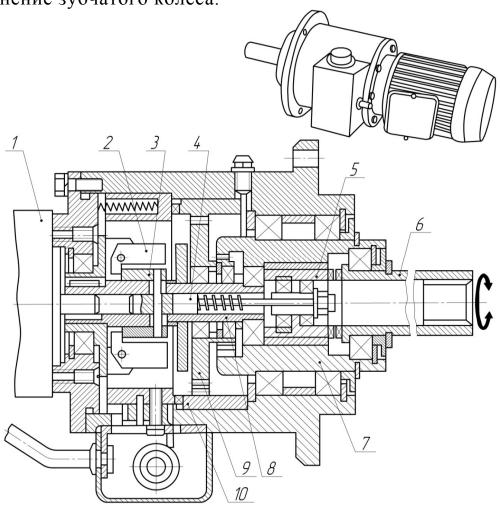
Электромеханический привод: 1 – электродвигатель; 2 – рычаг; 3 – втулка; 4 – шток; 5 – муфта; 6 – шлицевая втулка; 7, 9 – зубчатые колеса; 8 – эксцентриковый валик, 10 – планетарный механизм
